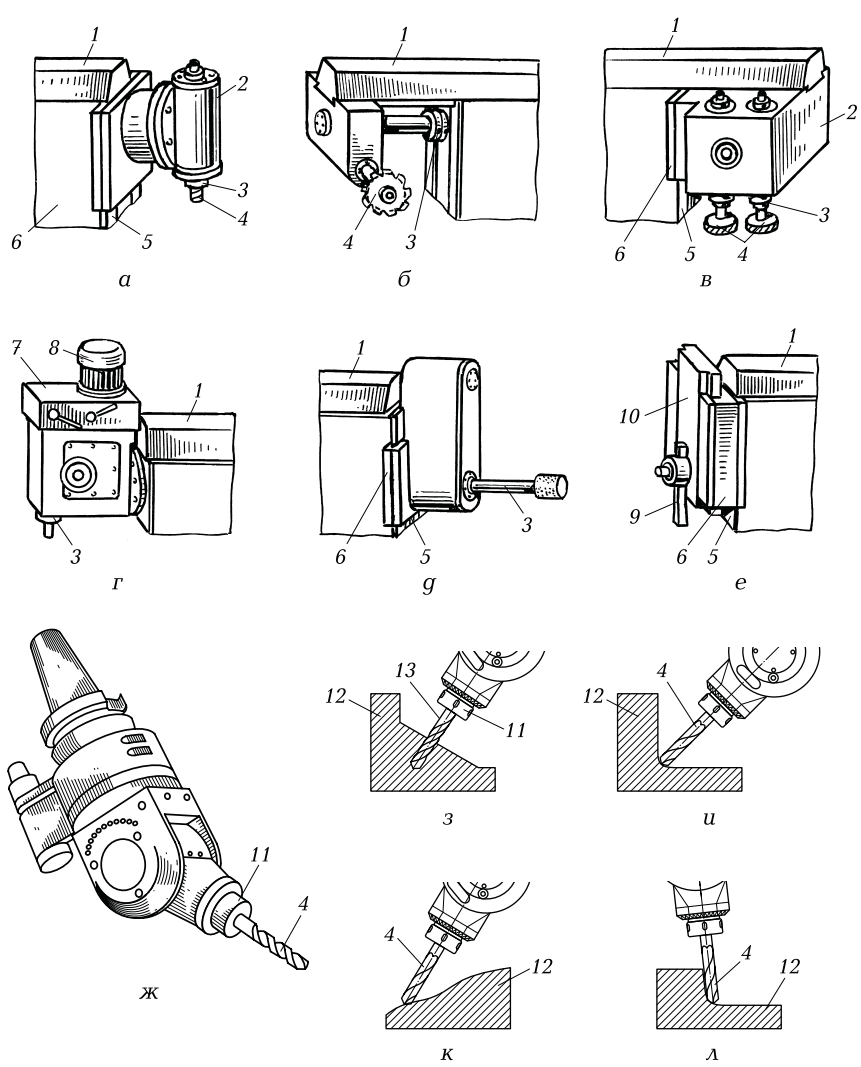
Специальные приспособления, расширяющие технологические возможности фрезерных станков (а...ж), и схемы обработки заготовок с помощью ускорительной головки (з...л):
